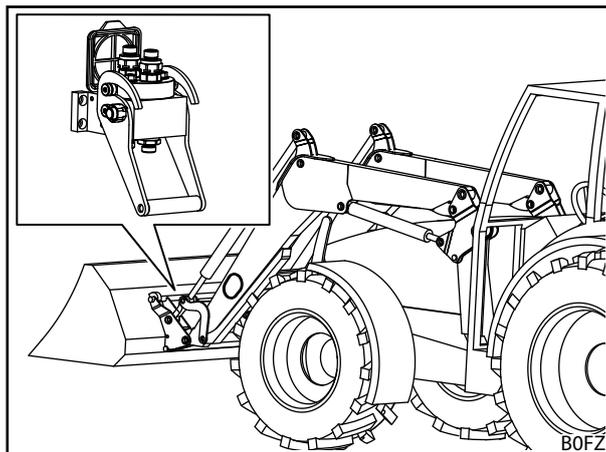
Dispositivo Fix per attrezzo: posizione sul caricatore frontale
